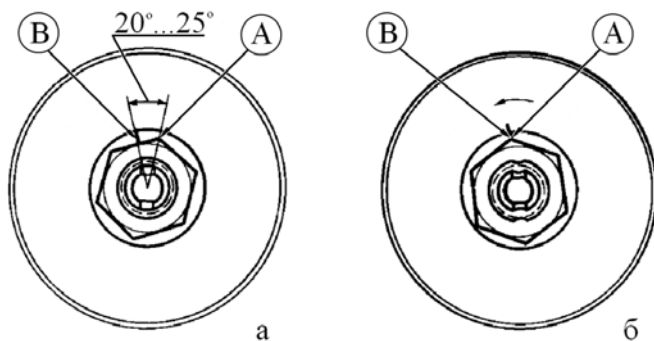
Затягивание и регулировка подшипников ступицы переднего колеса:
